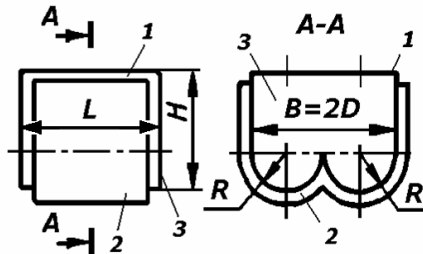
Схема корпусу змішувача: 1 – середня частина; 2 – сорочка; 3 – торцева стінка
